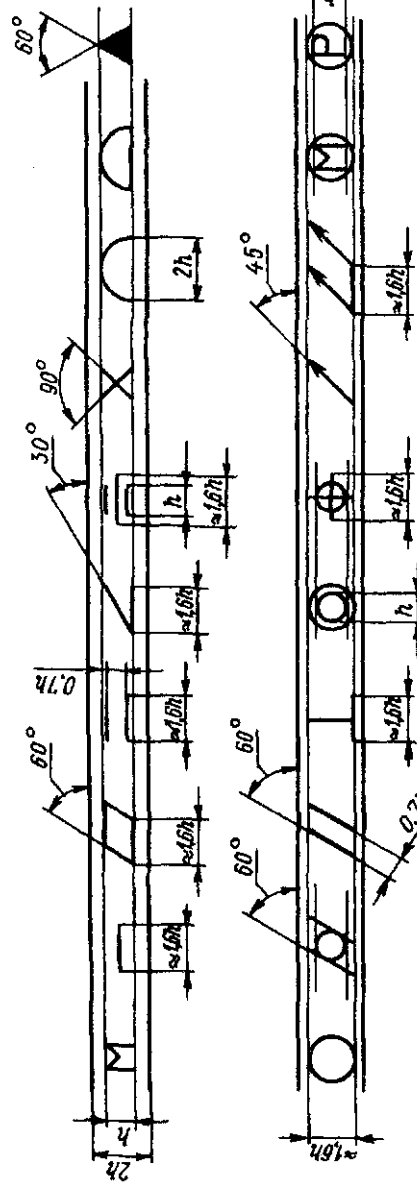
Размеры знаков для обозначения вида допусков формы и расположения
